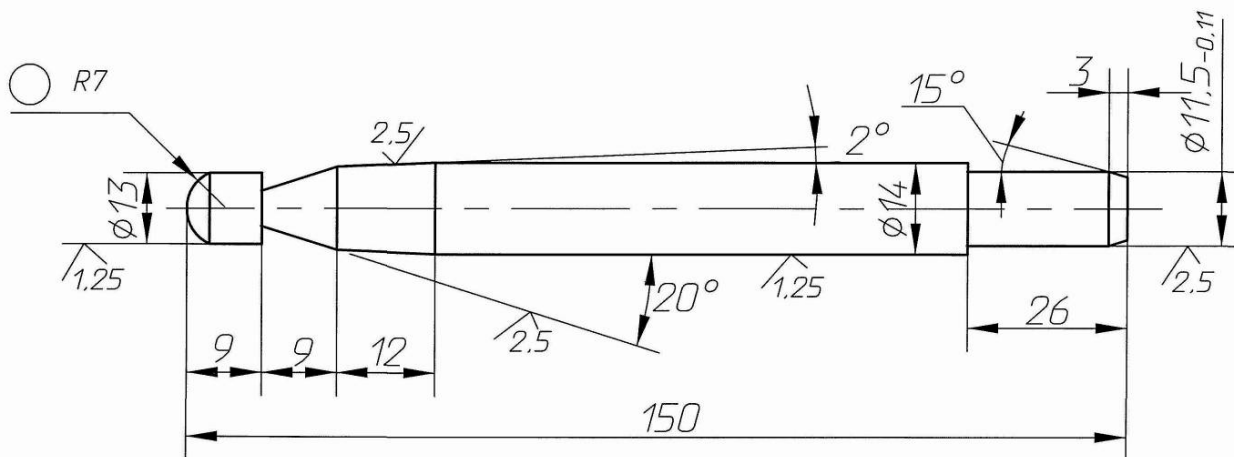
Направляющая оправка для установки крышки шестерен распределения
